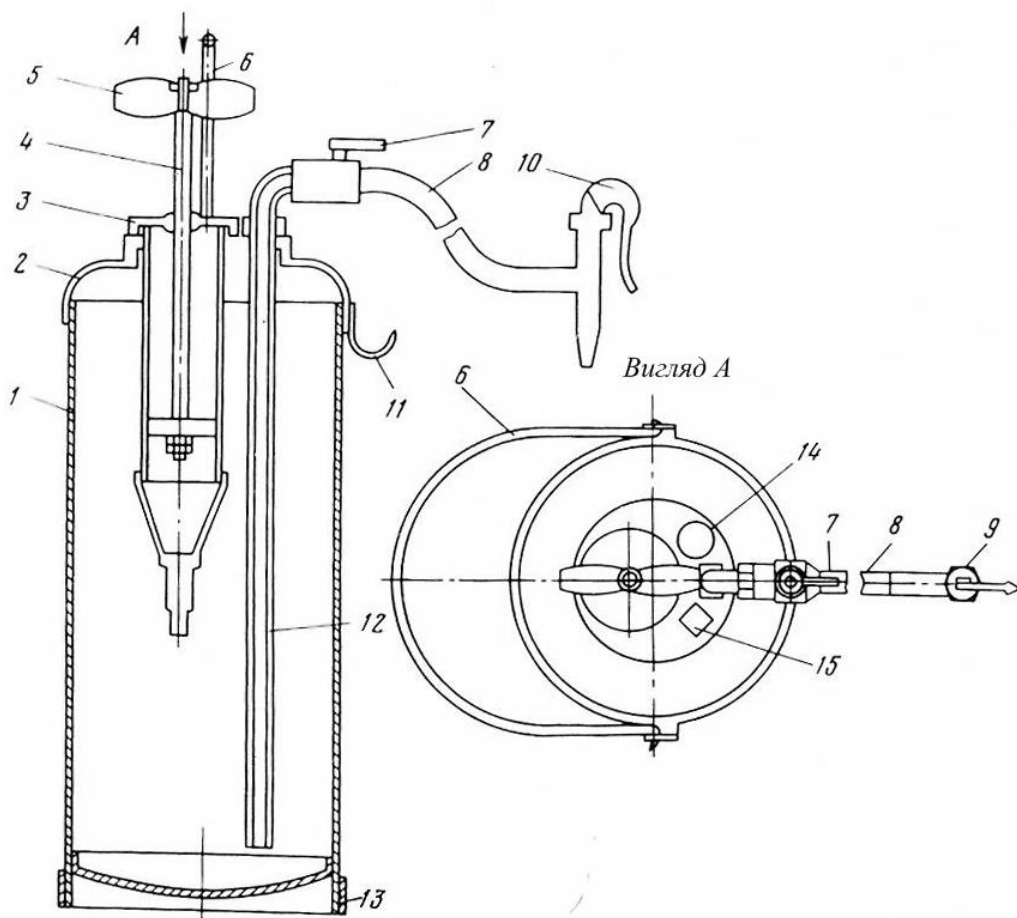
Пневматичний бачок: 1 – циліндр; 2 – днище верхнє; 3 – повітряний насос; 4 – шток; 5 – рукоятка; 6 – ручка; 7 – кран; 8 – гумовий рукав; 9 – наконечник з кульовим клапаном; 10 – ричаг; 11 – гачок; 12 – трубка; 13 – обичайка; 14 – випускний отвір; 15 – заливний пристрій
